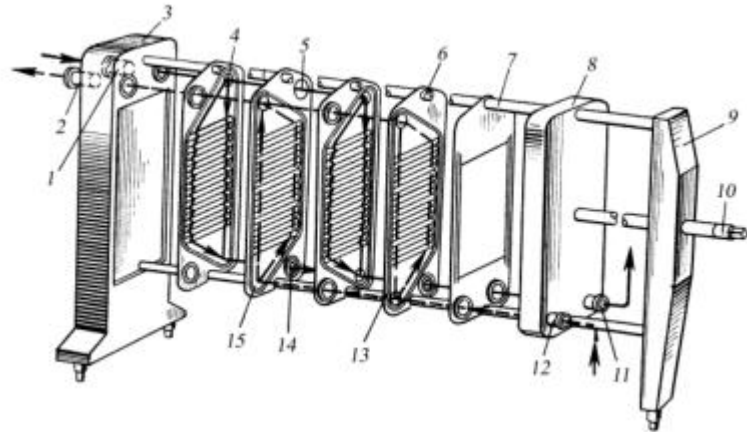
Пластинчастий теплообмінник: 1, 2, 11, 12 – штуцера; 3 – передня стійка; 4 – верхній кутковий отвір; 5 – кільцева гумова прокладка; 6 – обмежувальна пластина; 7 – штанга; 8 – натискна плита; 9 – задня стійка; 10 – гвинт; 13 – гумова прокладка; 14 – нижній кутковий отвір; 15 – теплообмінна пластина
